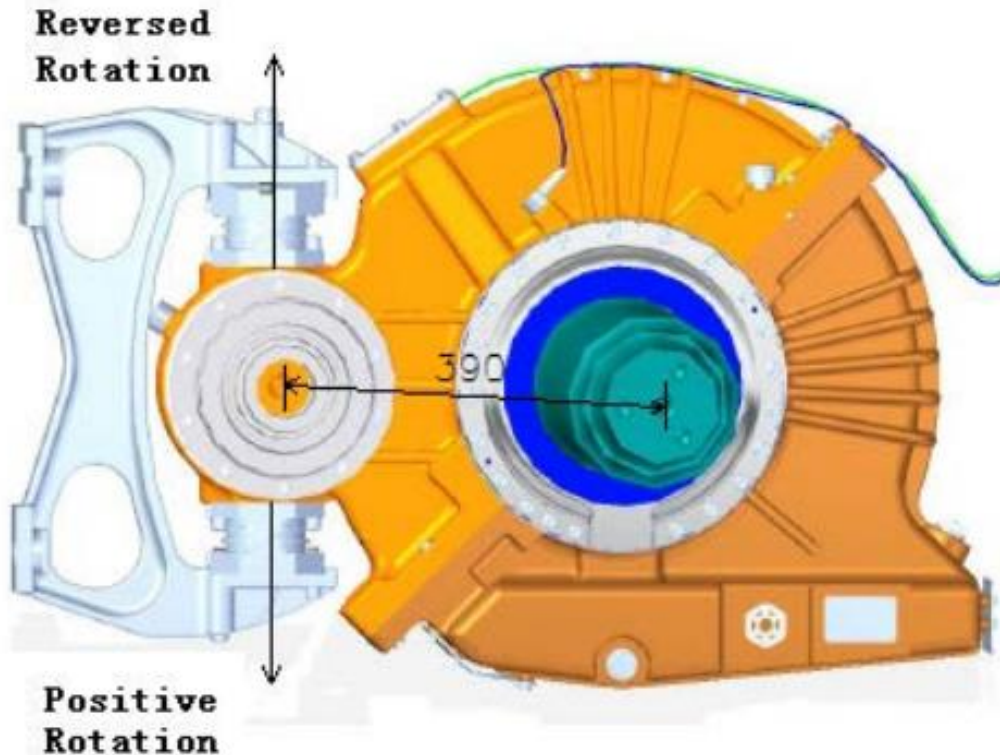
Кріплення кронштейну до корпусу редуктора
